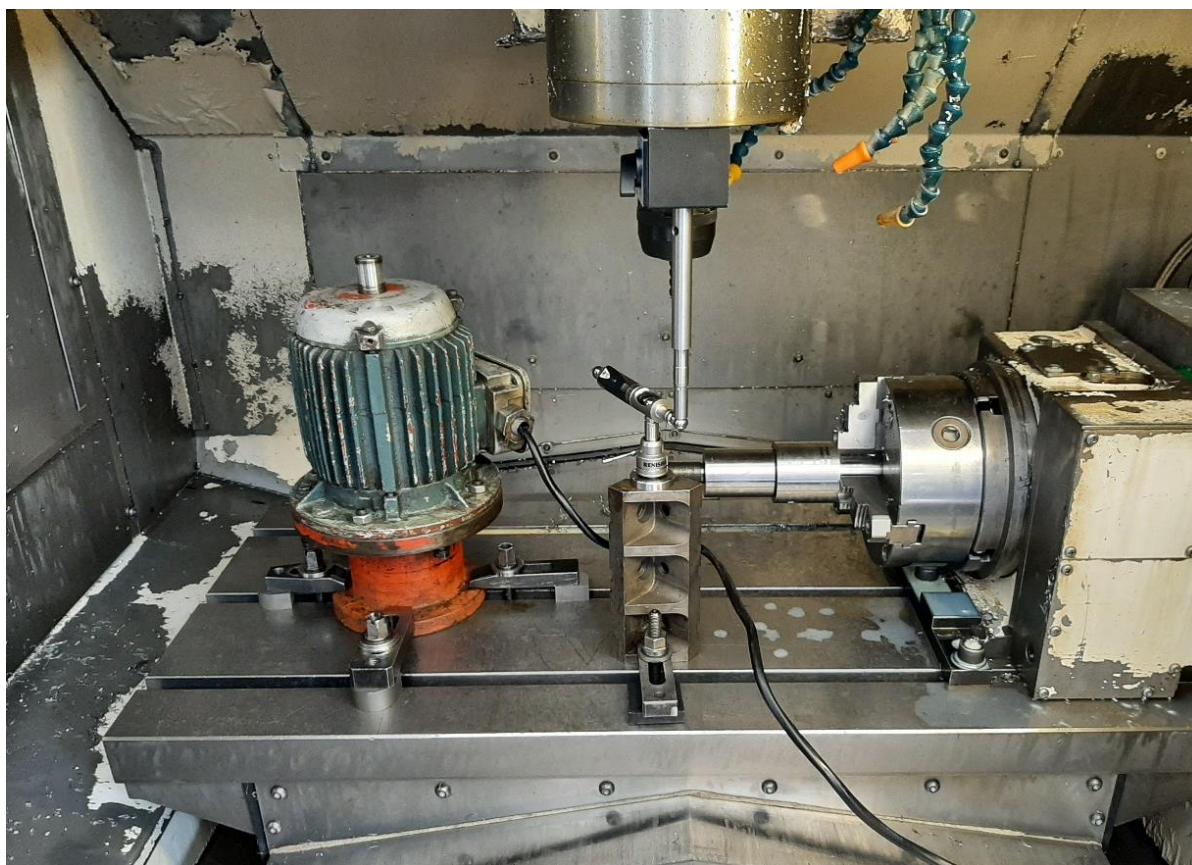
Внешний вид станка Okuma MB-400VA в процессе испытания
